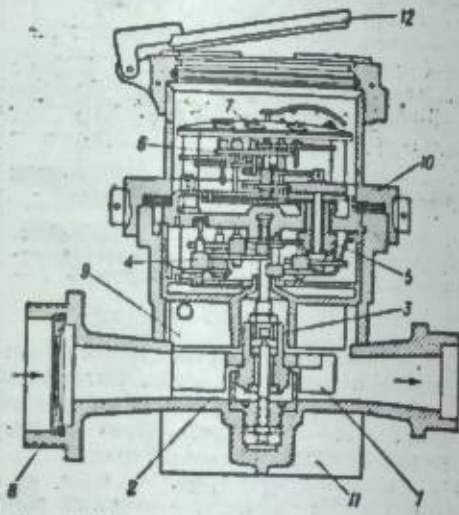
Разрез крыльчатого водомера: 1 — крыльчатка; 2 — камера крыльчатки; 3 — даточный подшипник; 4 — редуктор; 5 — сальник; 6 — механизм счетчика; 7 — пафферлат со стрелками; 8 — входной патрубок; 9 — редуктор; 10 — крышка корпуса; 11 — крылообразный выступ корпуса; 12 — крышка водомера.
